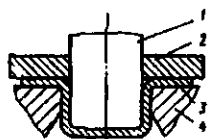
Схема вытяжки: 1 – пуансон; 2 – прижим; 3 – заготовка; 4 – матрица
